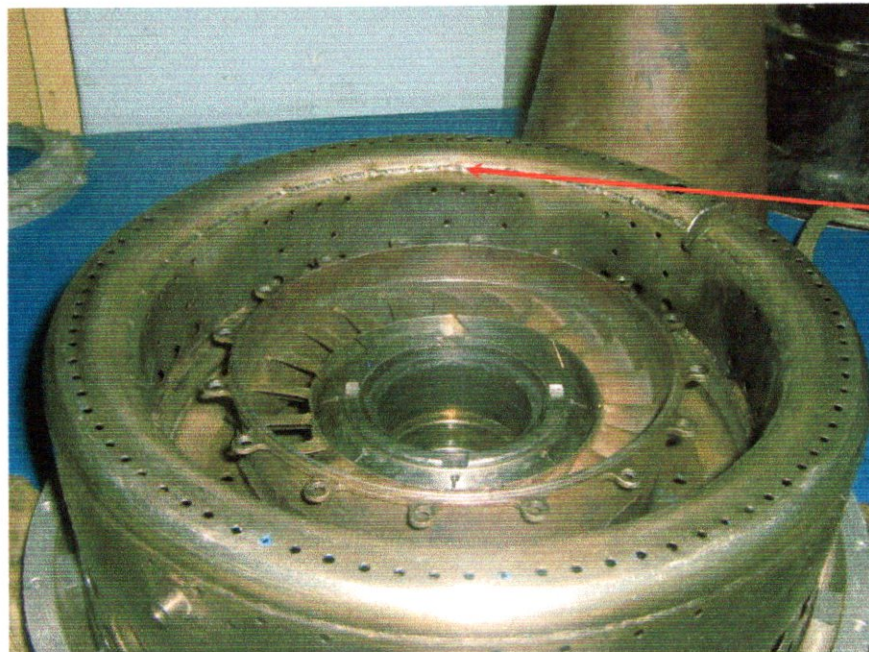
Soudure du réservoir de carburant en aluminium du moteur équipant l'hélicoptère MI-8.
